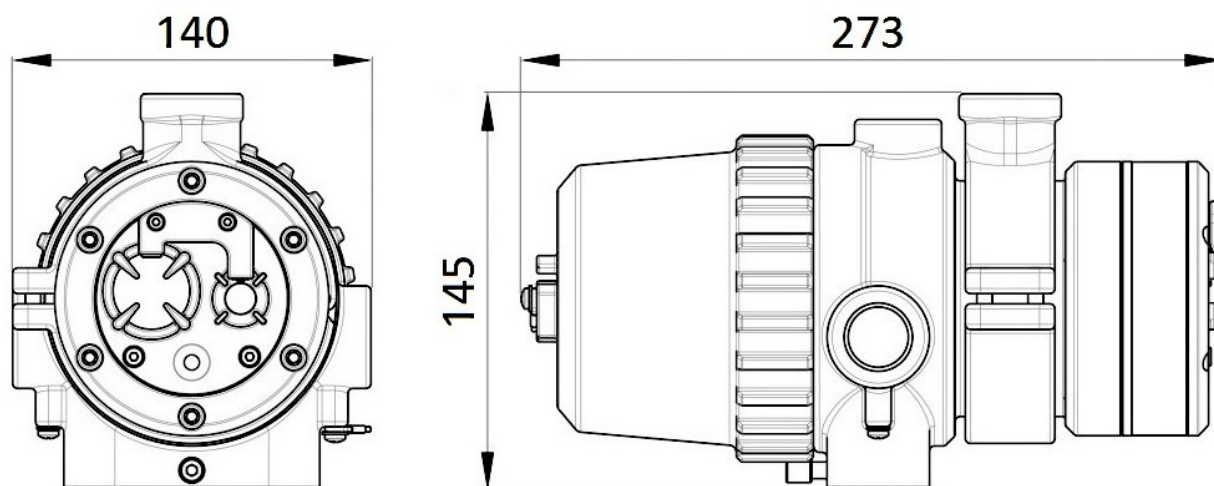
Габаритные размеры извещателя «СПАРК» в мм.
